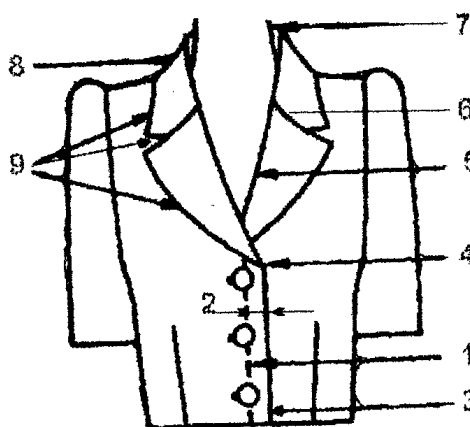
Parametri constructivi ai gulerului cu rever.
